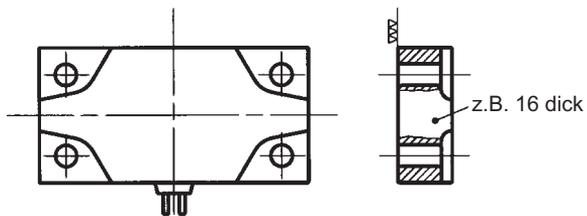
Heizplatte zum Aufschrauben auf den Heißkanal-Verteilerblock
